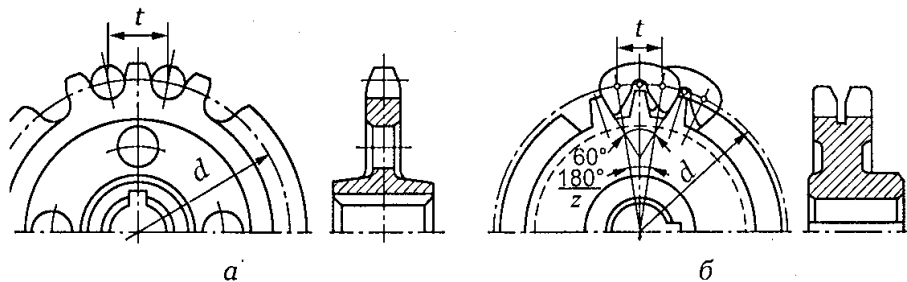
Типы звездочек для цепных передач: а — для втулочной и роликовой цепи; б — для зубчатой цепи
